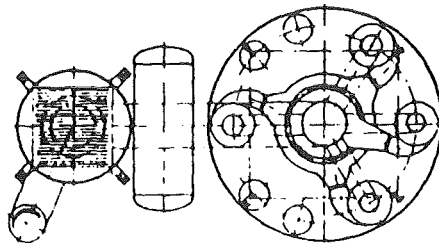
Druckaufgebener WSF-Dampferzeuger-Modul (90)
